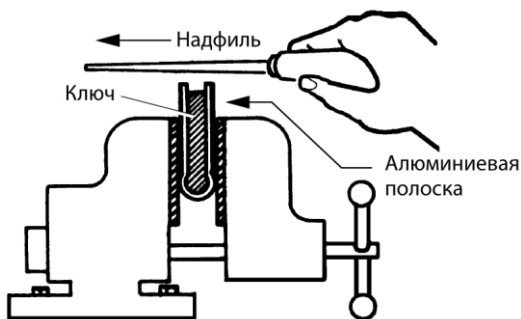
Шаблон ключа с бородкой можно изготовить из тонкой металлической полоски:
